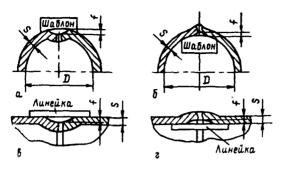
Контроль увода кромок продольных и кольцевых сварных соединений
